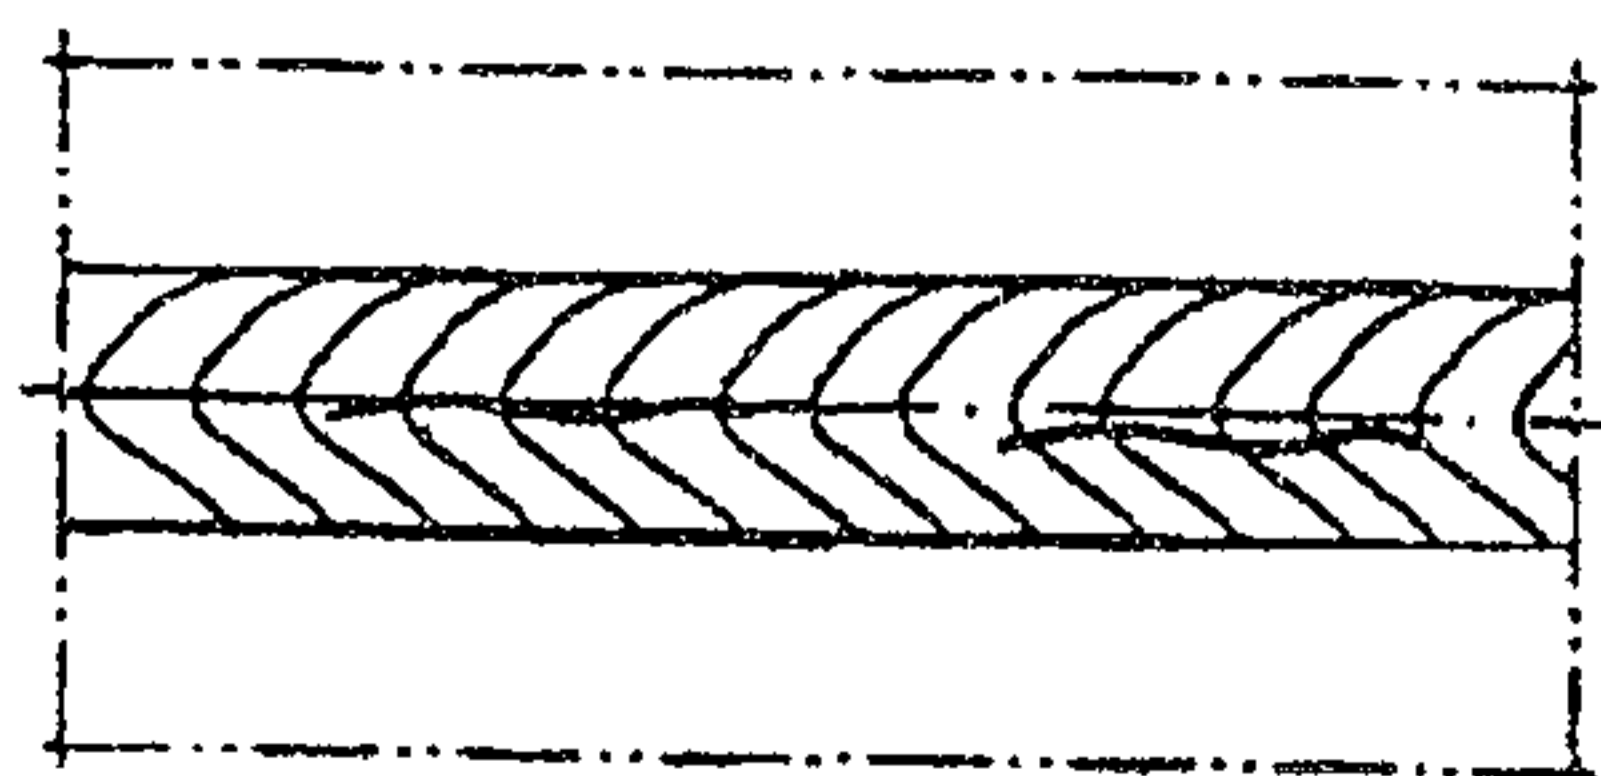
Продольные трещины сварного соединения
